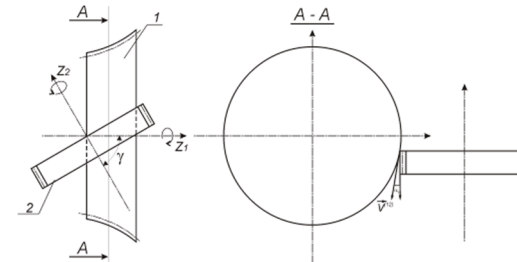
Схема формообразования квазиглобоидной заготовки
